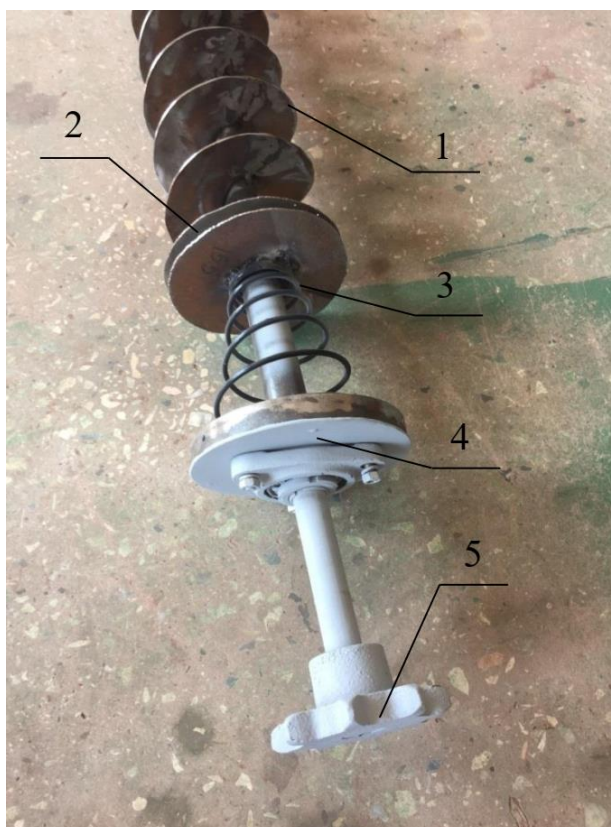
Загальний вигляд дожимного пристрою: 1 – витки шнека; 2 - притискний диск; 3 – пружина; 4 – заглушка; 5 – привідна зірочка
